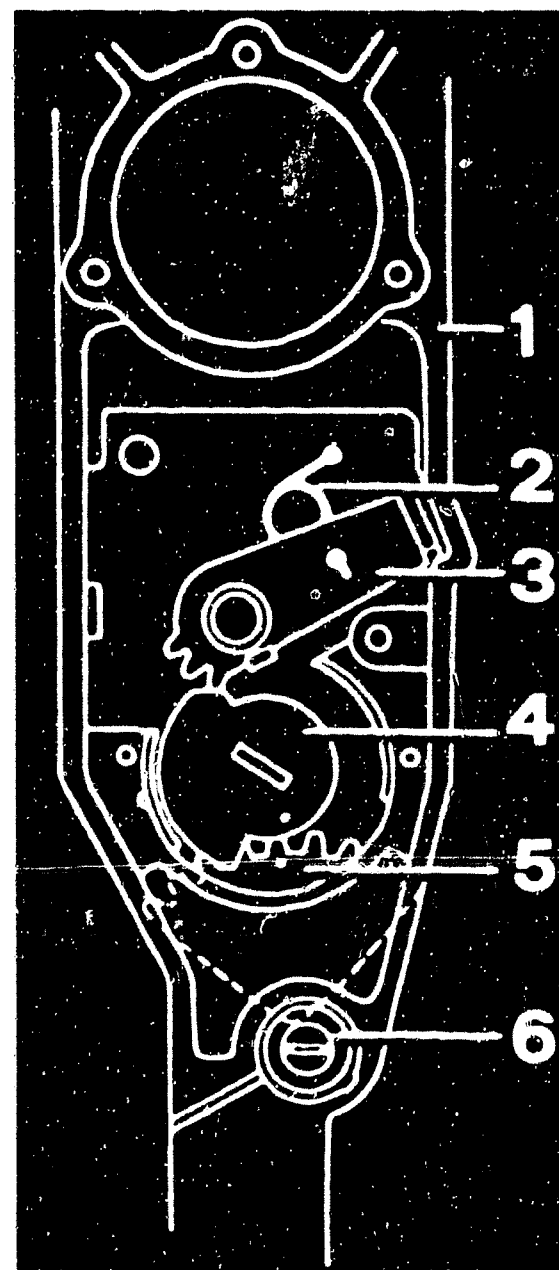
Beim Drehen des Zündschlüssels wird das Zahnsegment mitgedreht. Einzelteile des Zünd- und Schalthebelschlosses: 1 Gehäuse – 2 Feder – 3 Schlosszunge – 4 Zahnrad – 5 Zahnsegment – 6 Zündschloss.
